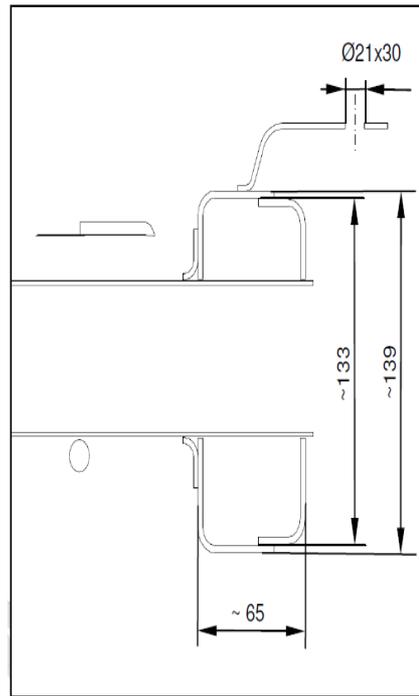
coupe R-R (Amarok SC/DC)
